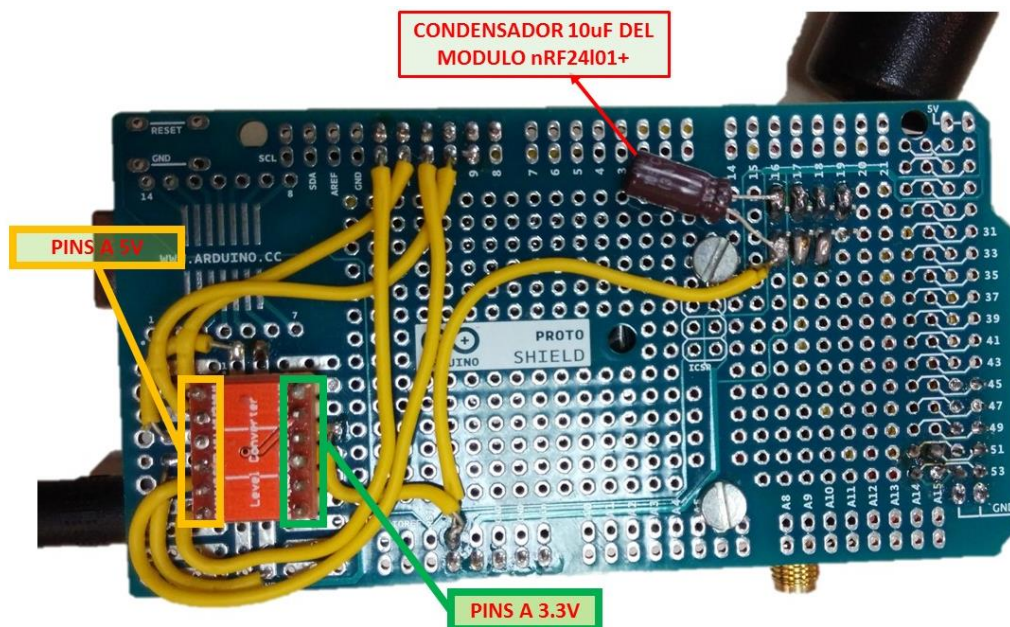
Vista exterior del protoshield con el conversor lógico y los cables soldados (Fuente: propia)
